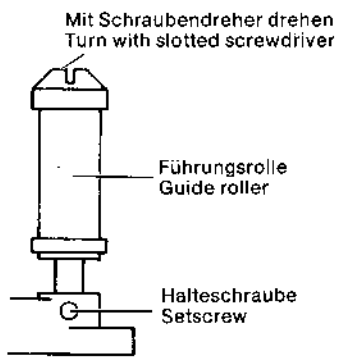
Führungsrollen-Höhenjustage / Guide roller height adjustment
